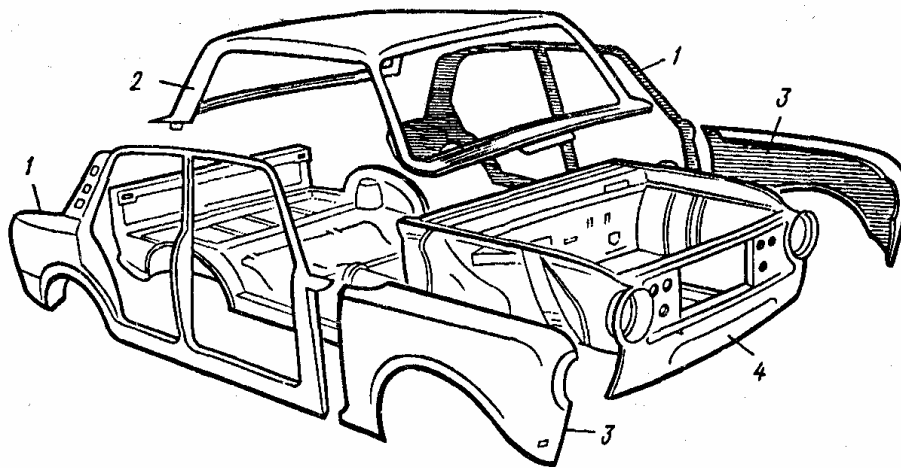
Элементы несущей конструкции корпуса кузова
